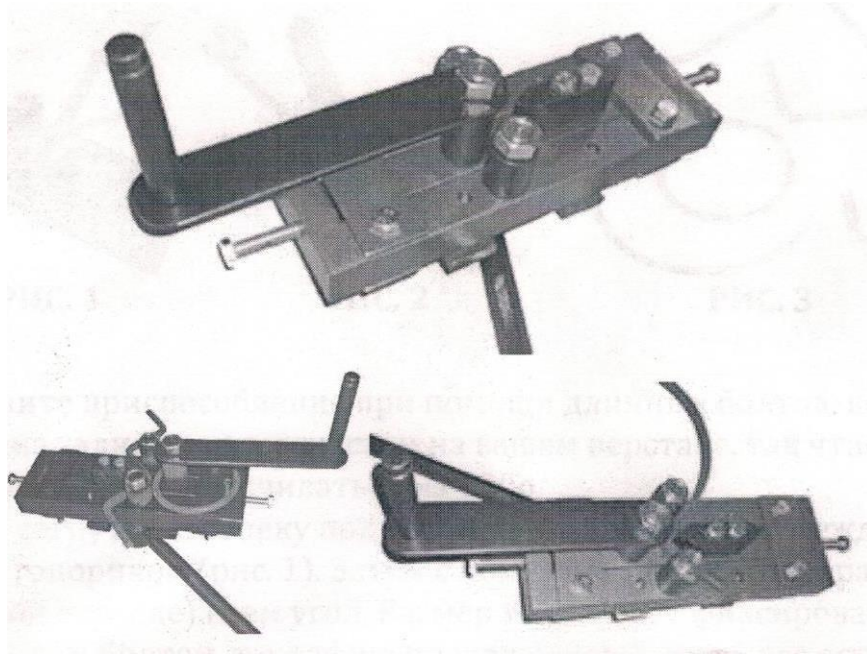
Общий вид инструмента для гибки металла «гнутик»
